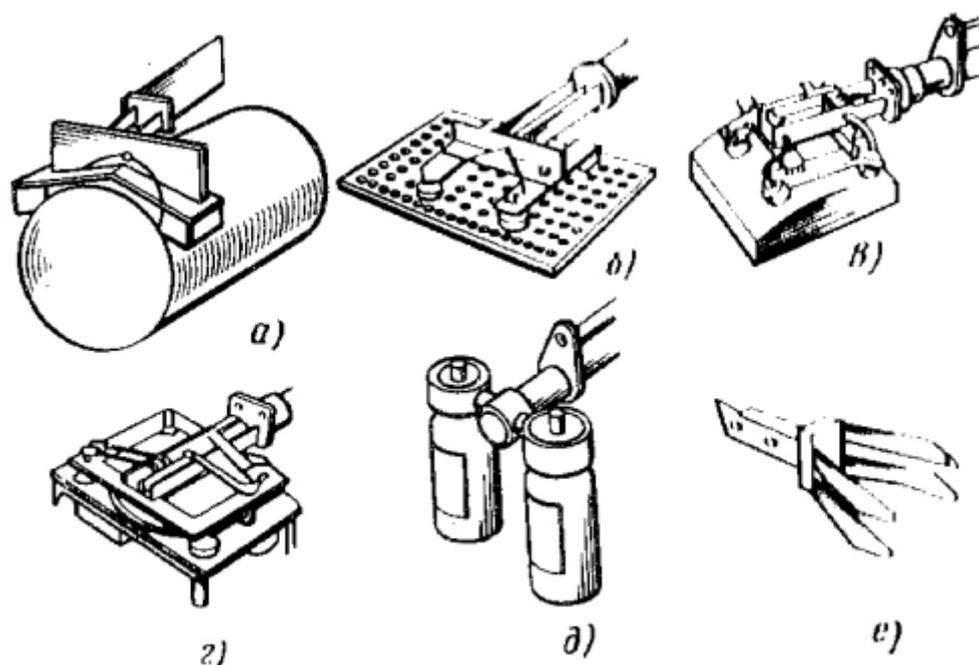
Захватные устройства: а и б – электромагнитные; в и г – вакуумные; д и е – с эластичными камерами.
